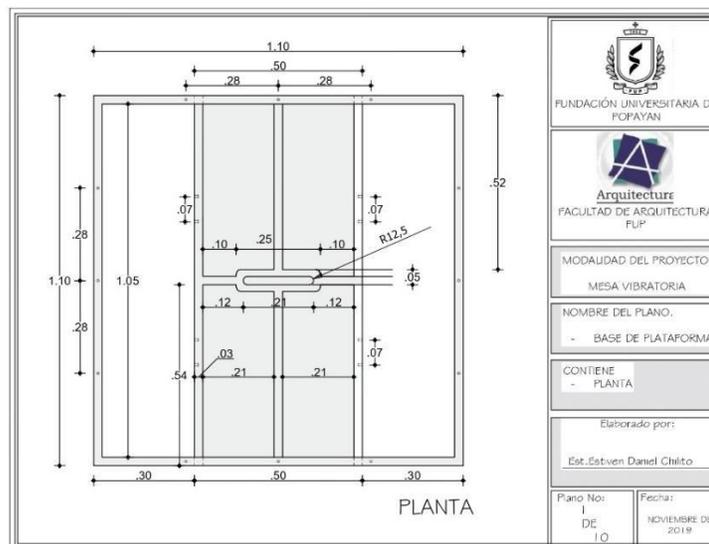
Planta de detalle plataforma base. *Fuente propia.
